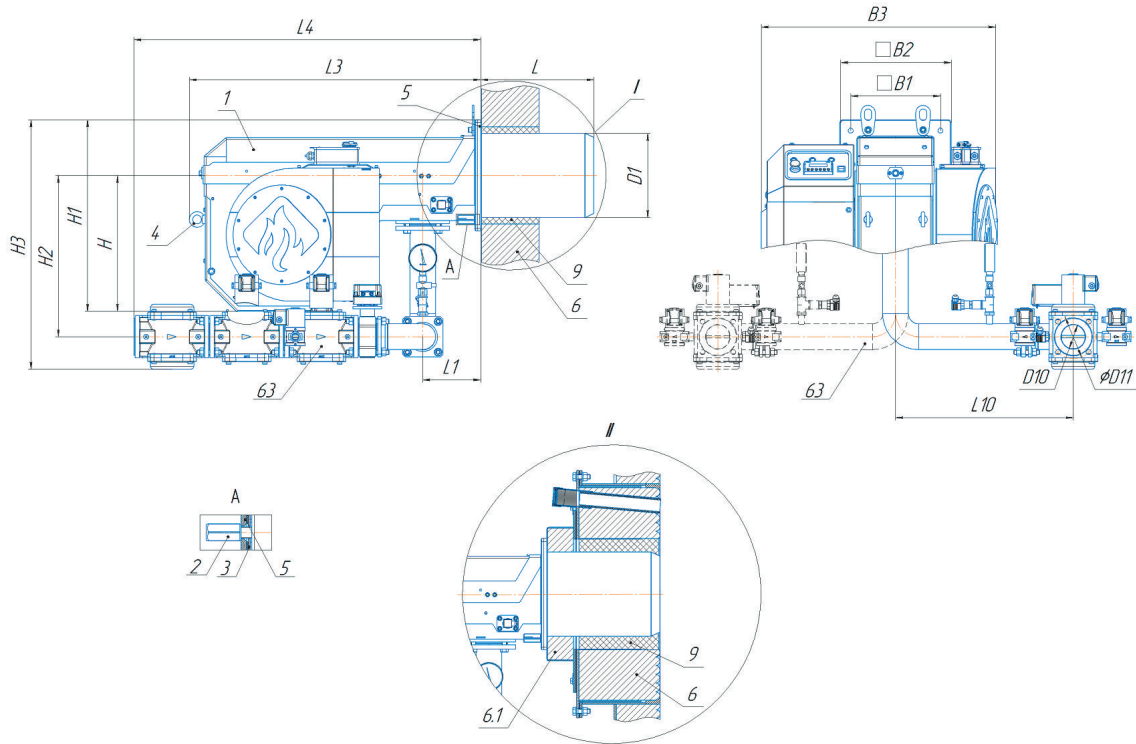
Габаритный чертеж горелок (размеры смотри Таблицу 11).
